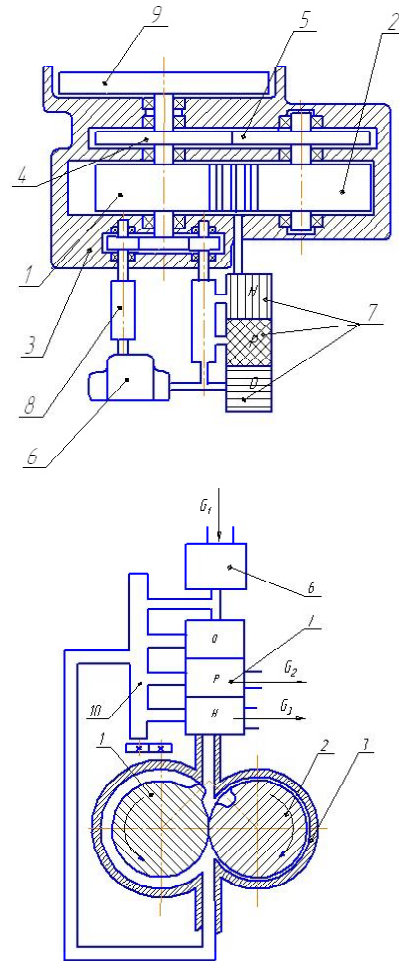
Двигун зовнішнього згоряння: 1 – ротор робочий; 2 – ротор перевідний; 3 – корпус; 4, 5 – зубчата передача; 6 – компресор; 7 – регенератор, нагрівач, охолоджувач; 8 – варіатор; 9 – маховик; 10 – дозатор-розподільник; G_1 – повітря, яке споживає двигун; G_2 – відпрацьоване робоче тіло; G_3 – відпрацьовані гази нагрівача
